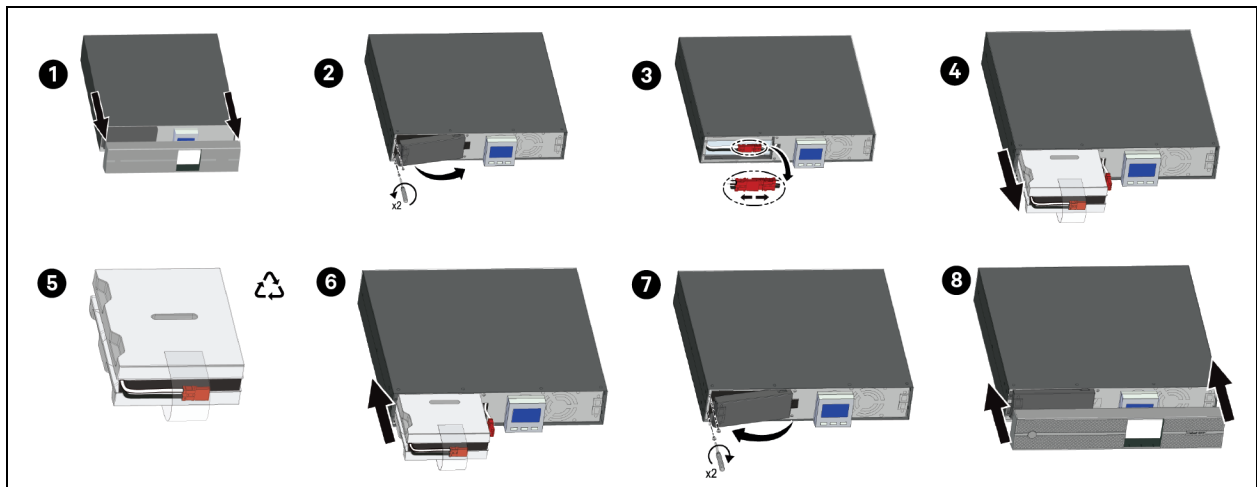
Reemplazo de batería - SAI en rack/torre
